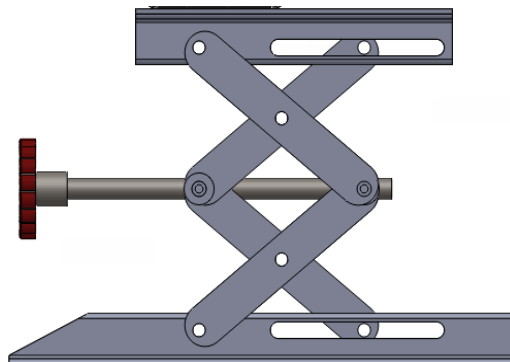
27.-Dimensiones geométricas plancha elevable [Autores]
